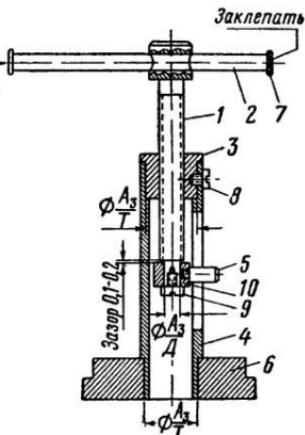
Модель винтового механизма (схема соединения деталей): 1 — винт; 2 — ручка; 3 — гайка; 4 — труба; 5 — стопор; 6 — основание; 7 — шайба; 8 — стопорный винт; 9 — винт; 10 — кольцо.
